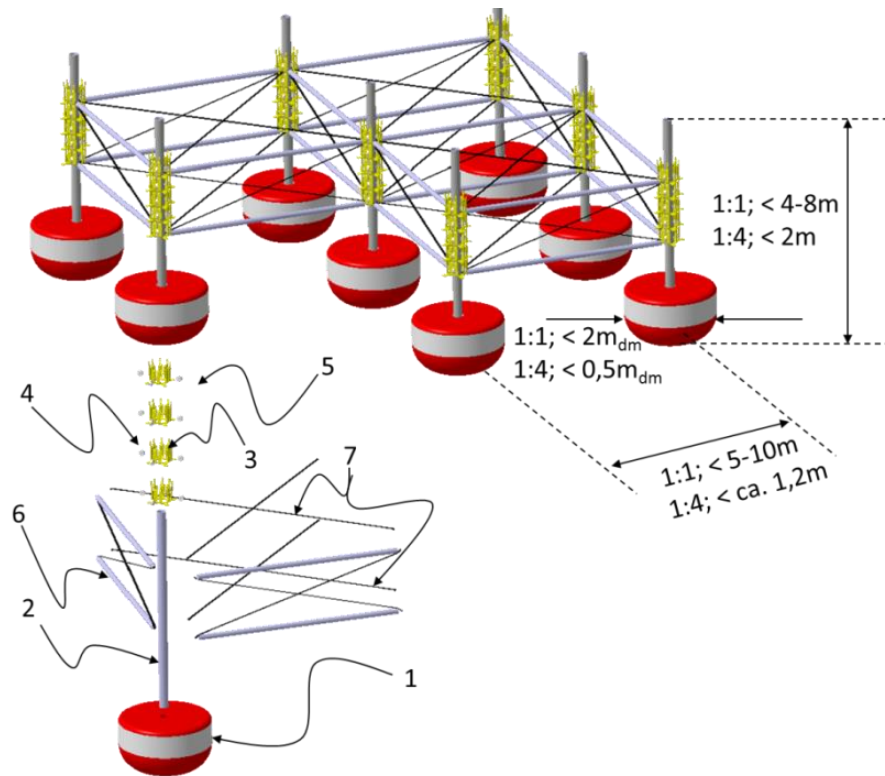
Wellenkraftwerk mit neun Modulen und einem Modul in Explosionszeichnung
